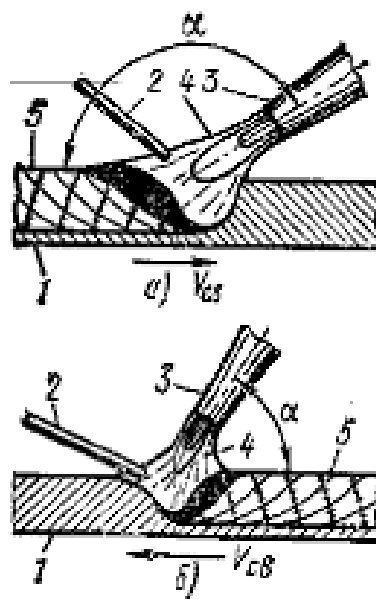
Схема газовой сварки: а – правым способом, б – левым способом
